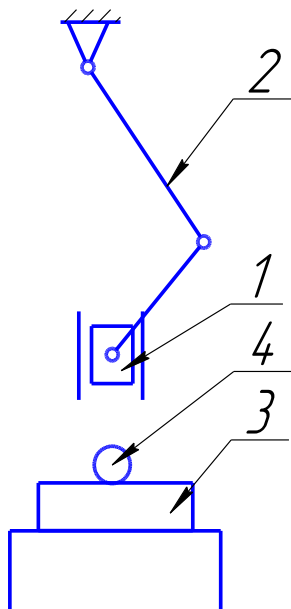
Схема КГШП: 1 - ползун, 2 - кривошипный механизм, 3 - штамп, 4 - заготовка.
